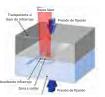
Diagrama de la soldadura por transmisión láser
